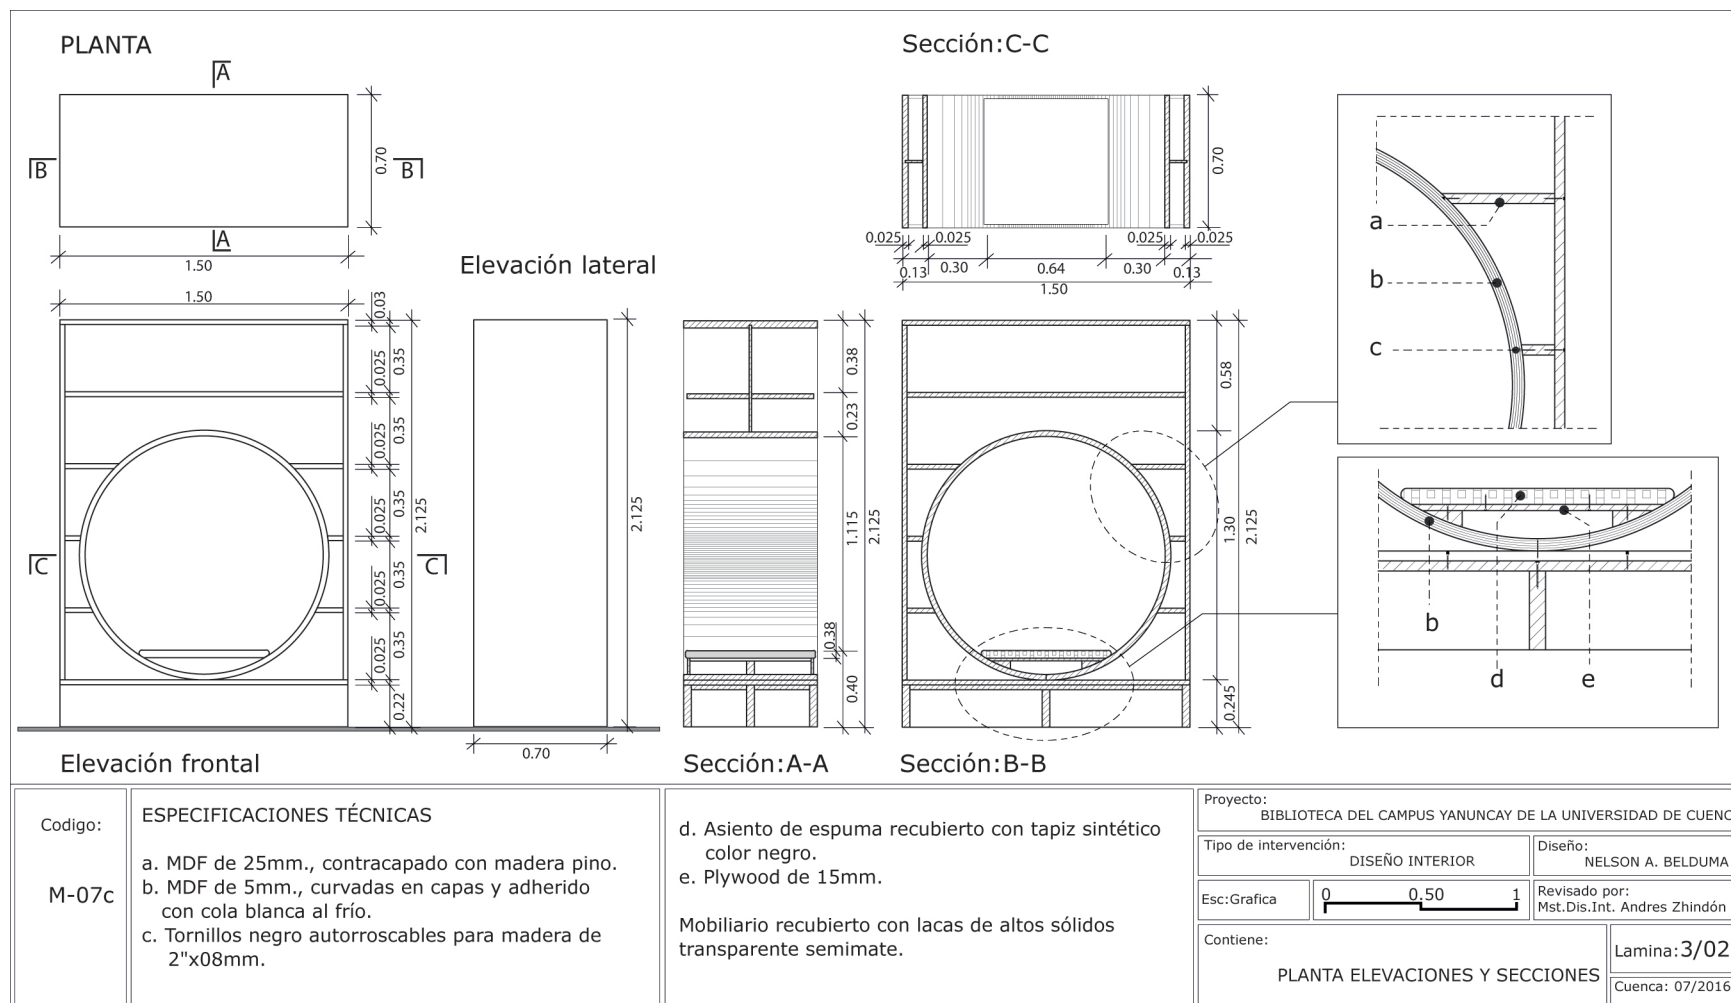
Planta, elevaciones y secciones. Estanterías. M-07c.
